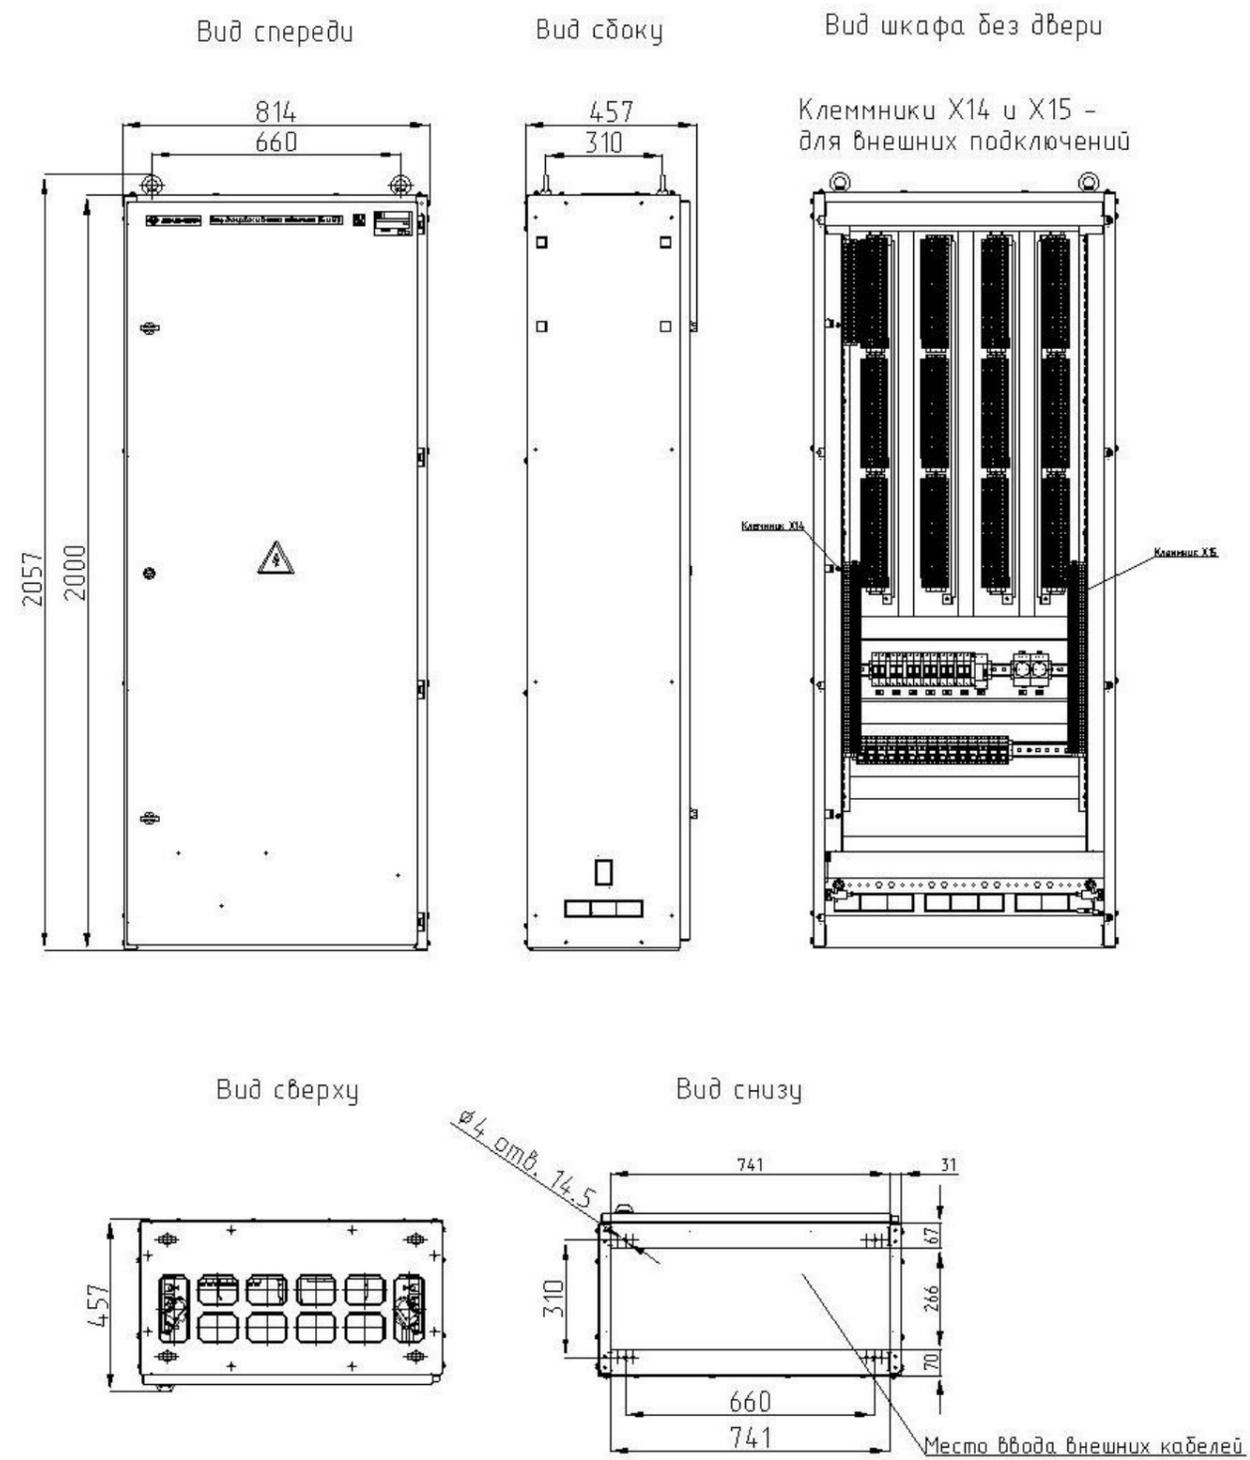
Габаритный чертеж шкафа блокировок и внешних подключений
